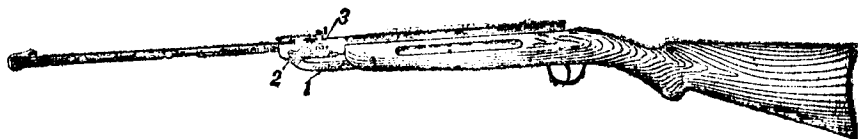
Наша пневматическая винтовка. 1 — рычаг; 2 — ось рычага; 3 — ось винтовки.
